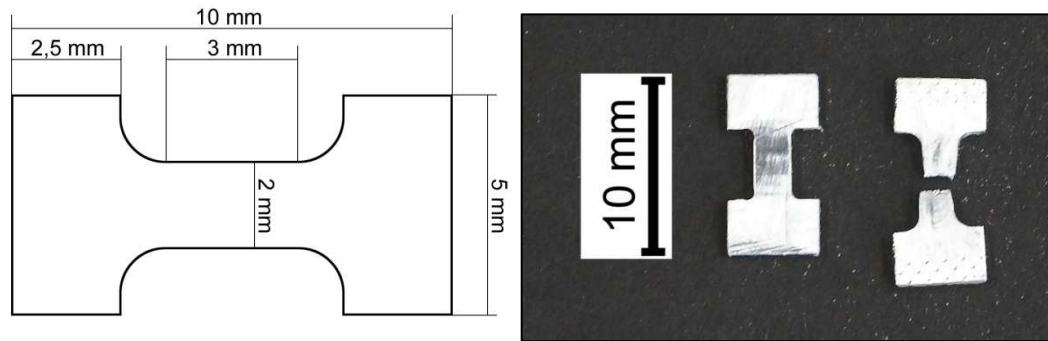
Probengeometrie der Flachzugproben (links), Probe vor und nach dem Zugversuch (rechts)
